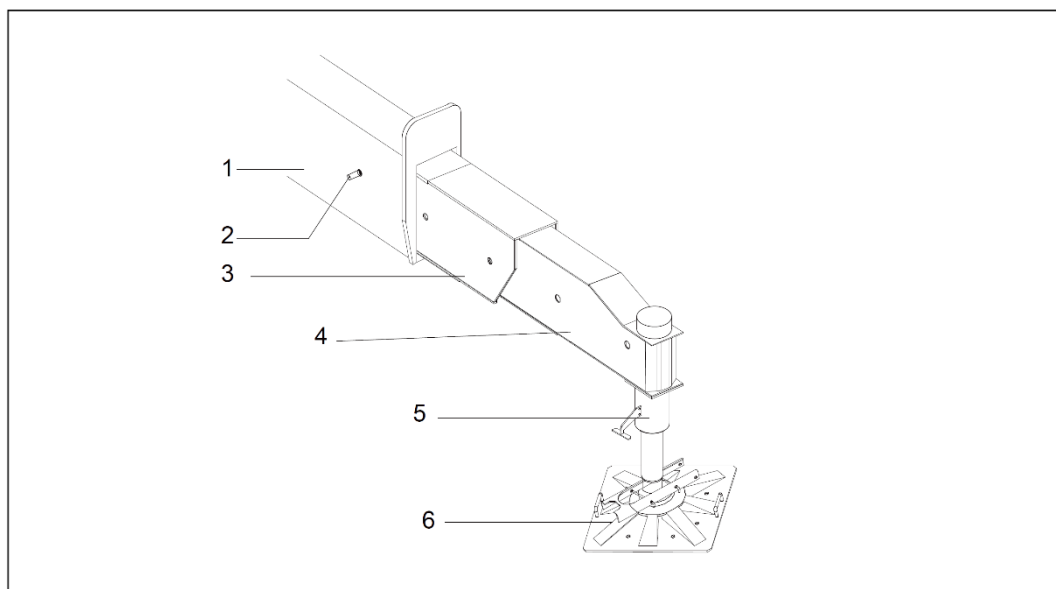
Seções de viga deslizante 1 e 2 estendidas
